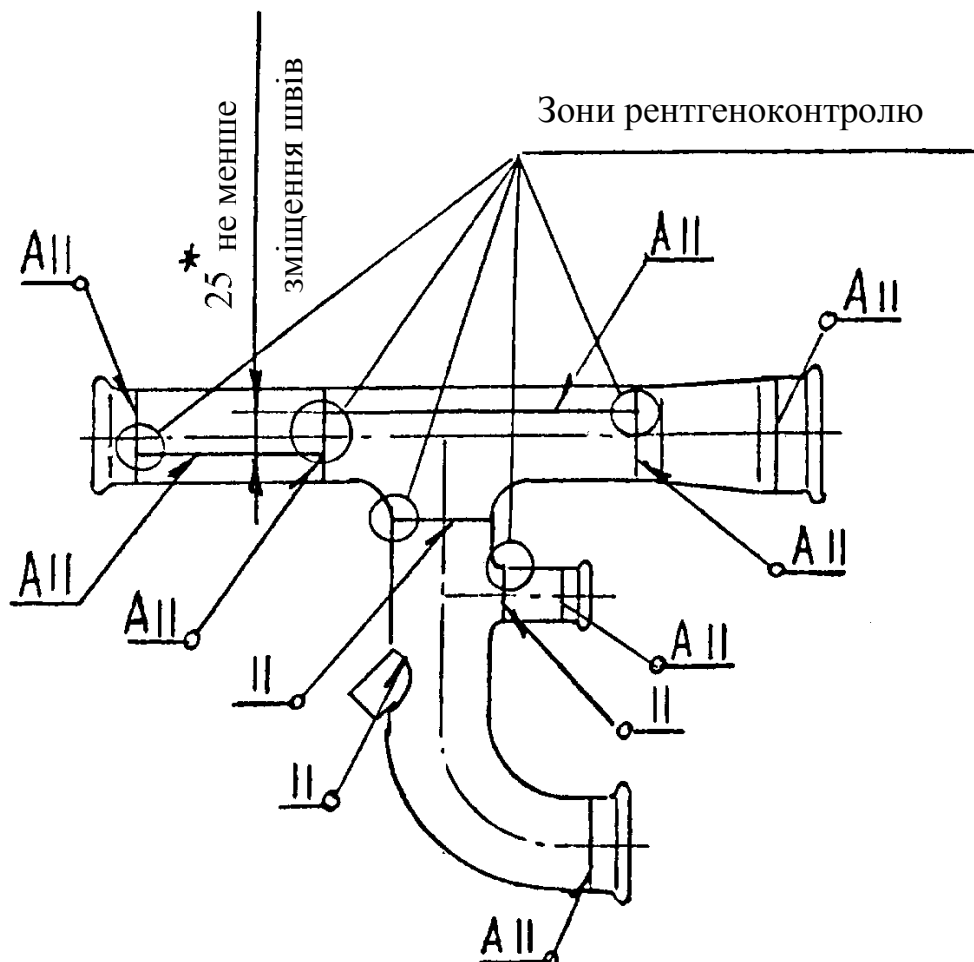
Розташування зварених швів і графічне зображення способів зварювання на креслениках для всіх матеріалів. Зони рентгеноконтролю для корозійностійких сталей (* – крім випадків, обумовлених у креслениках)
